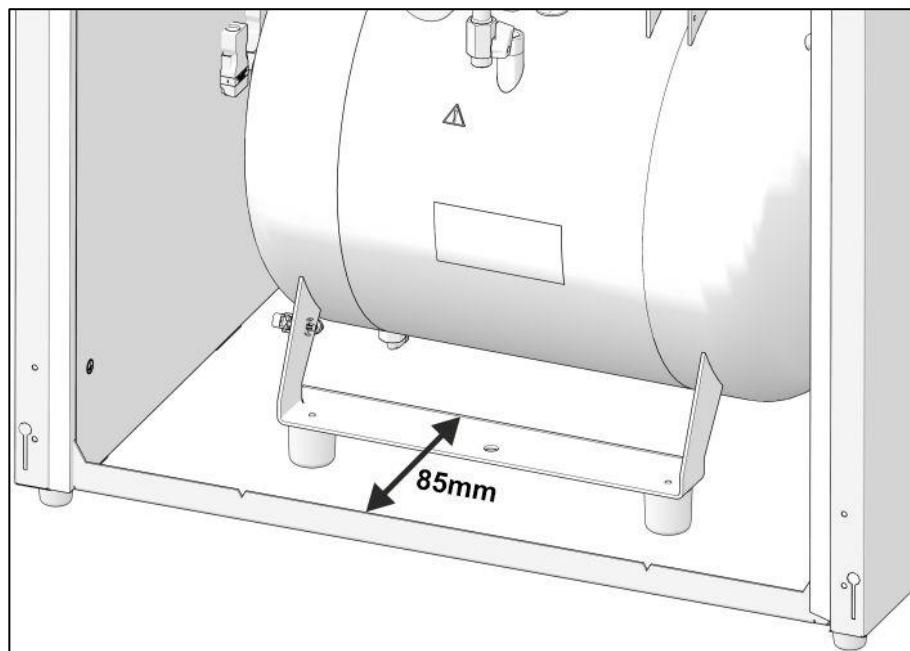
Umiestnenie kompresora pre elektrické zapojenie
